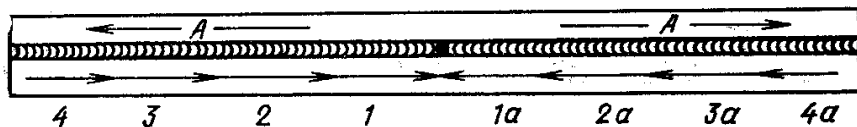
Сварка длинных швов обратноступенчатым способом от середины к концам шва.
